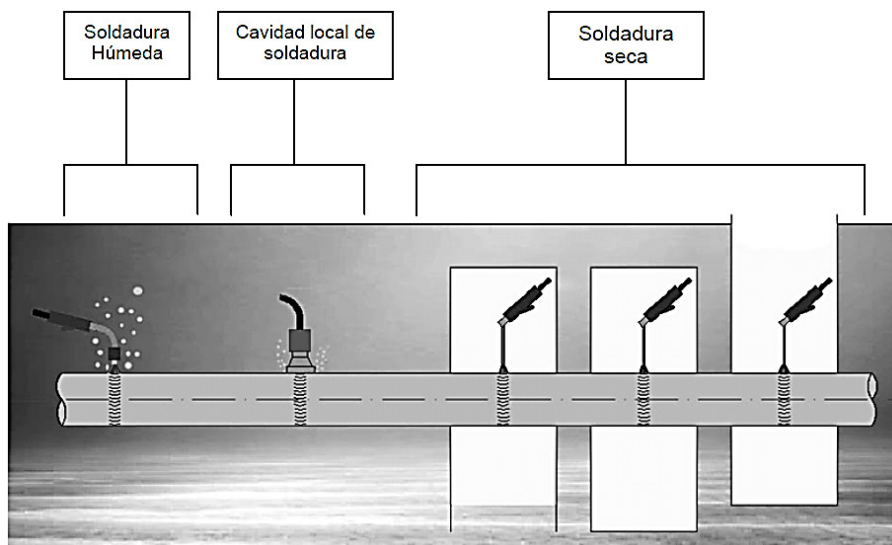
Técnicas existentes de soldadura submarina^[14]
